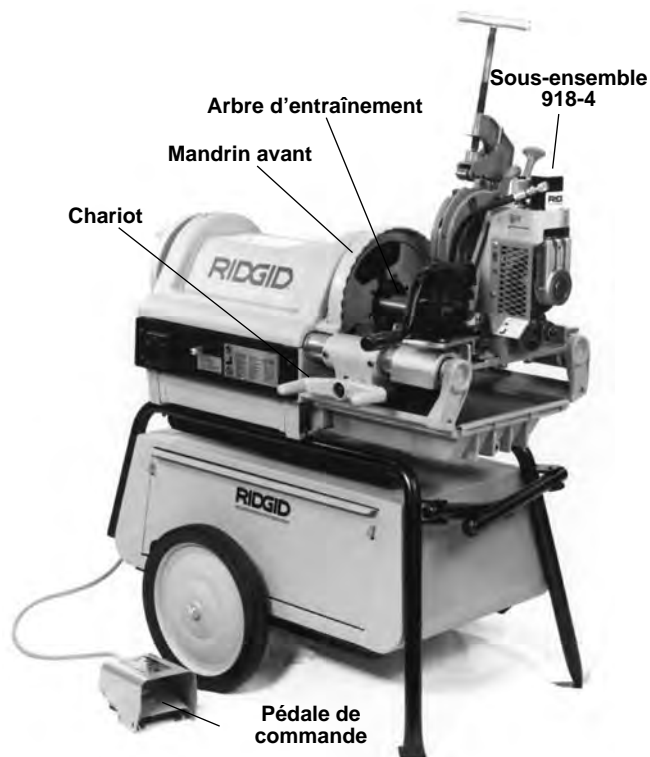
Rainureuse à galets n° 918-4 sur machine à fileter n° 1224
